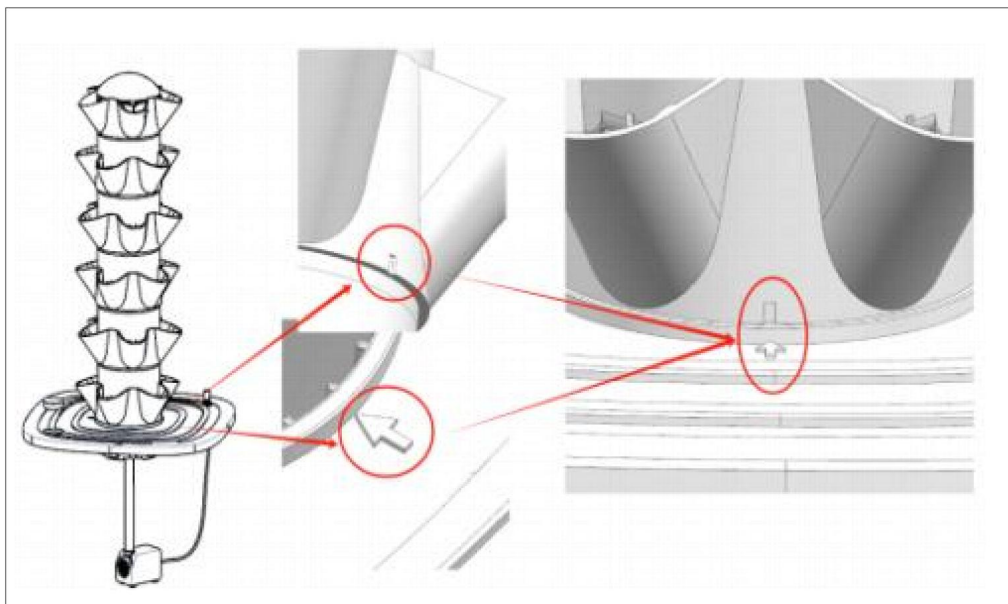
Far passare la pompa dell'acqua attraverso il centro del coperchio del secchio come mostrato, quindi assemblare la torre dell'acqua al coperchio del secchio.
